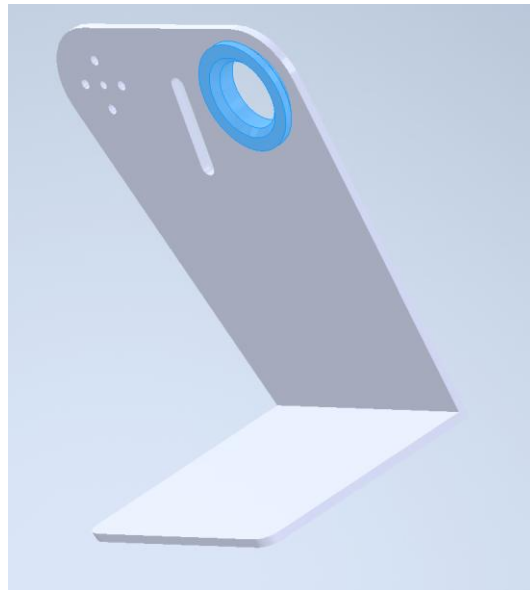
Design* da estrutura de fixação do sistema de sobrealimentação elétrica com o acoplamento da flange para o motor elétrico (a azul)
